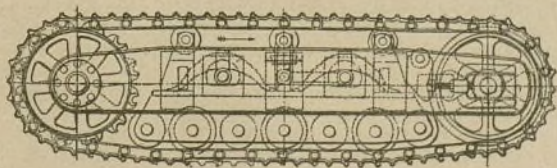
Cadena rastreadora montada totalmente sobre muelles y cojinetes Tractor Clayton.
